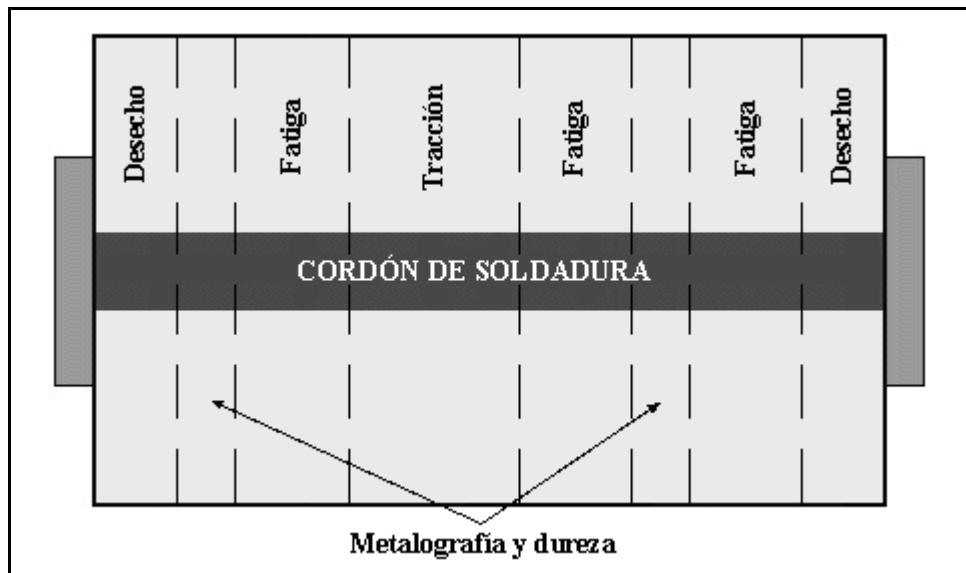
Esquema de los cortes para probetas de la junta soldada.
